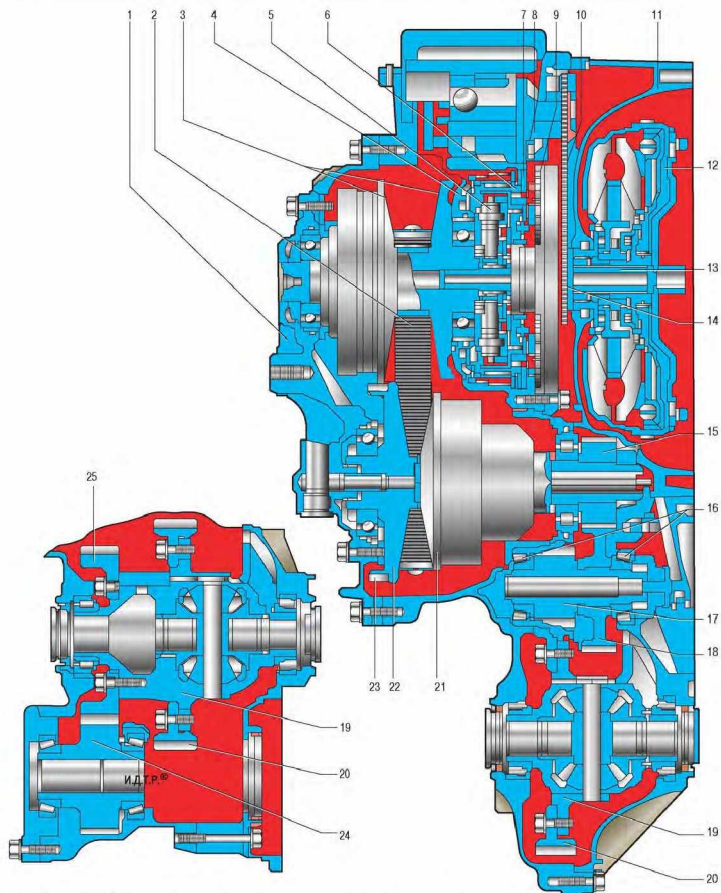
Бесступенчатый вариатор REOF10A: 1 – боковая крышка вариатора; 2 – стальной гибкий ремень; 3 – подвижные полушкивы первичного вала; 4 – кожух планетарной передачи; 5 – центральная шестерня планетарной передачи; 6 – фрикцион; 7 – фрикционный тормоз; 8 – насос рабочей жидкости вариатора; 9 – цель привода насоса; 10 – зубчатый барабан привода насоса; 11 – кожух гидротрансформатора; 12 – гидротрансформатор; 13 – первичный вал; 14 – зубчатый барабан цели привода насоса; 15 – ведущая шестерня вторичного вала; 16 – подшипники; 17 – шестерня редукционной передачи; 18 – промежуточная шестерня; 19 – корпус дифференциала; 20 – шестерня главной передачи; 21 – подвижные полушкивы вторичного вала; 22 – шестерня стояночного положения; 23 – спутниковая шестерня планетарной передачи; 24 – шестерня привода выходного вала раздаточной коробки; 25 – шестерня отбора мощности для привода задних колес
